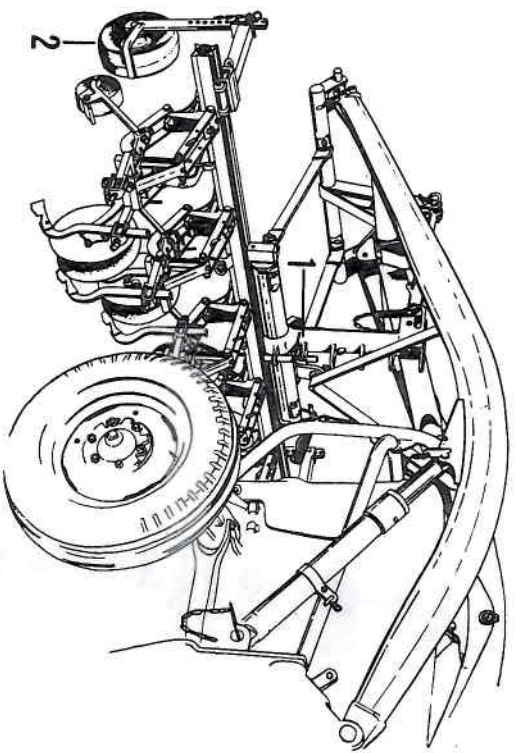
Frontlader mit RAU-KOMBI-Hackmaschine
